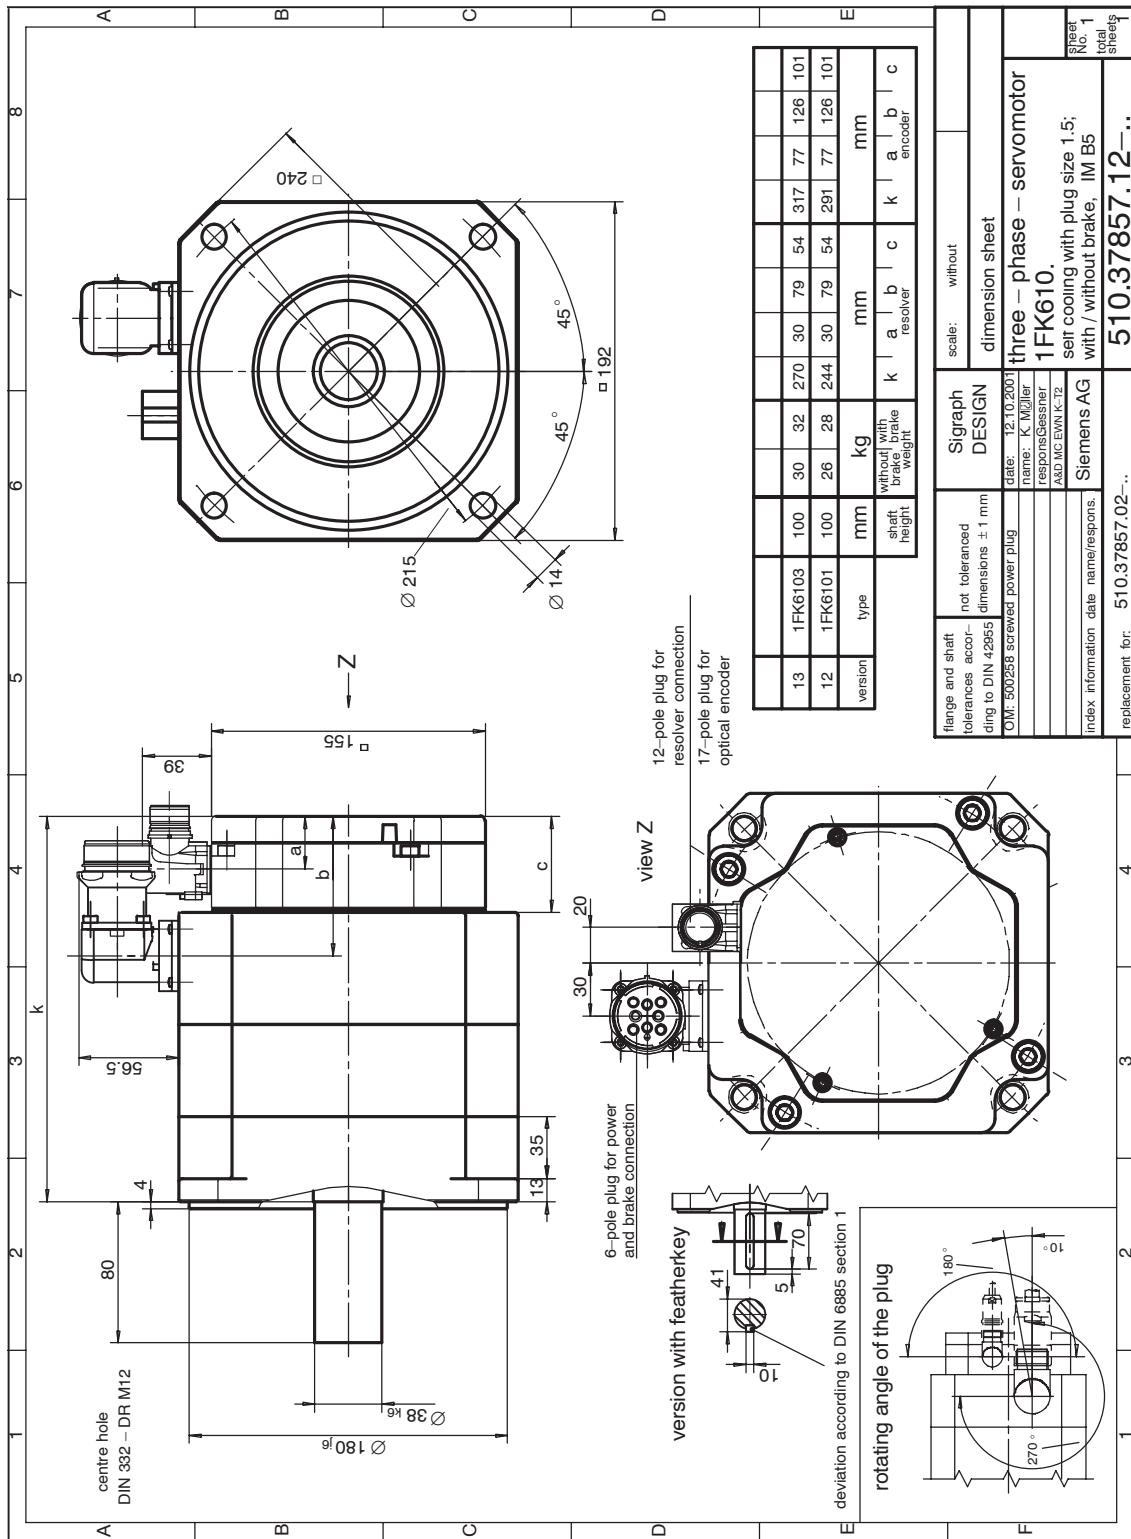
1FK610□ Standard,selbstgekühlt mit Stecker Größe 1.5
